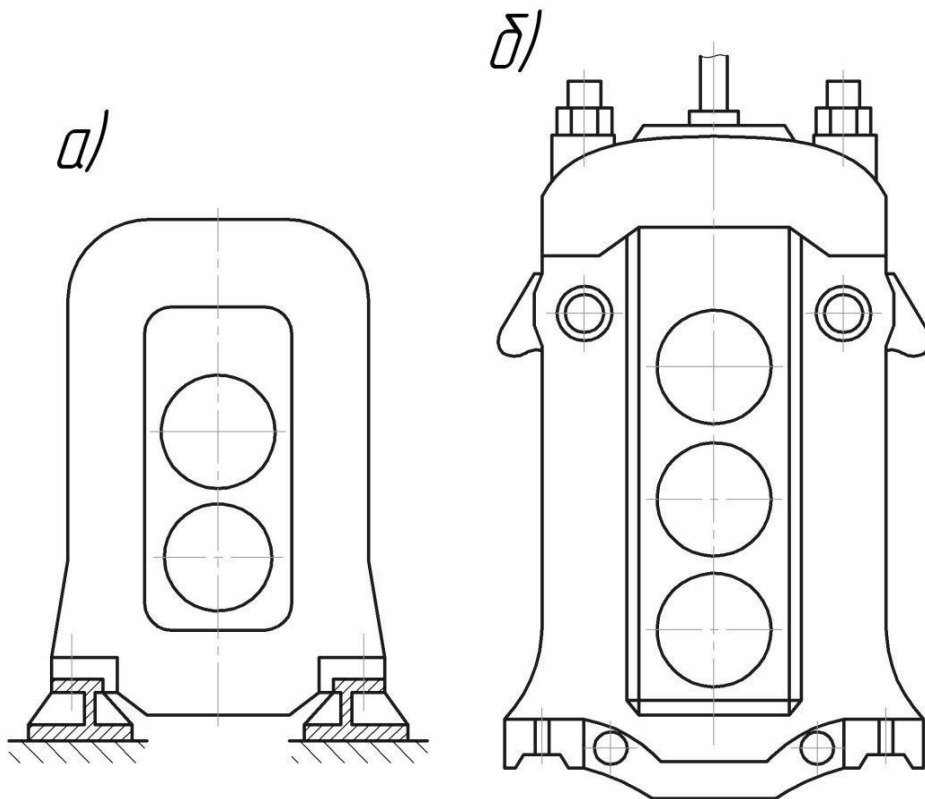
Робочі кліті прокатного стану: а) двовалкові; б) тривалкові
